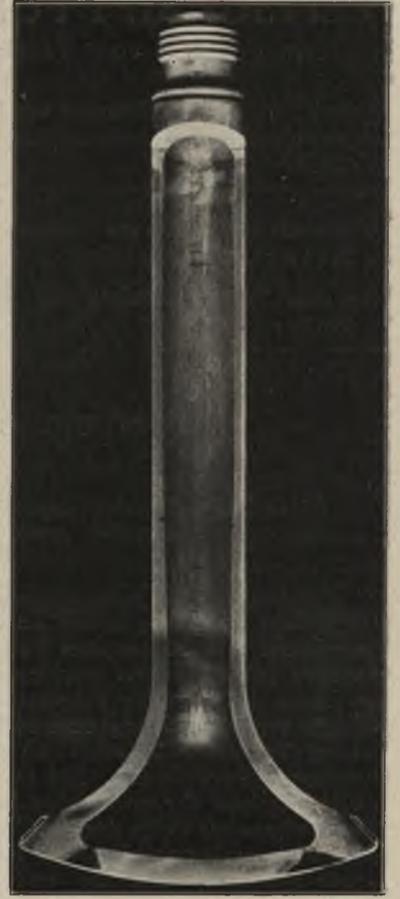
Hohlteller-Auslaßventil mit eingeschweißtem Boden aus einem deutschen Flugmotor. (× rd. 0.75.)
